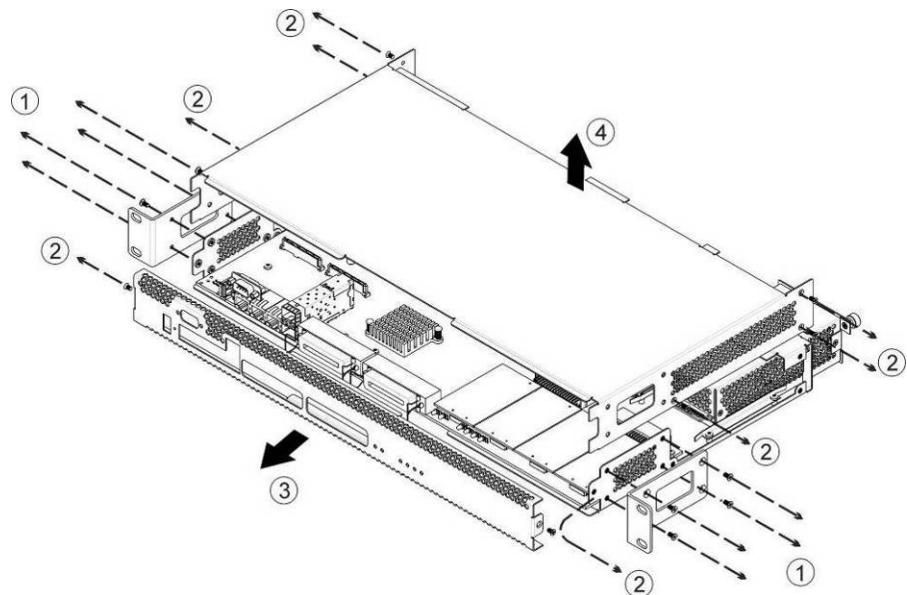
а – Порядок вскрытия корпуса SMG-1016М
